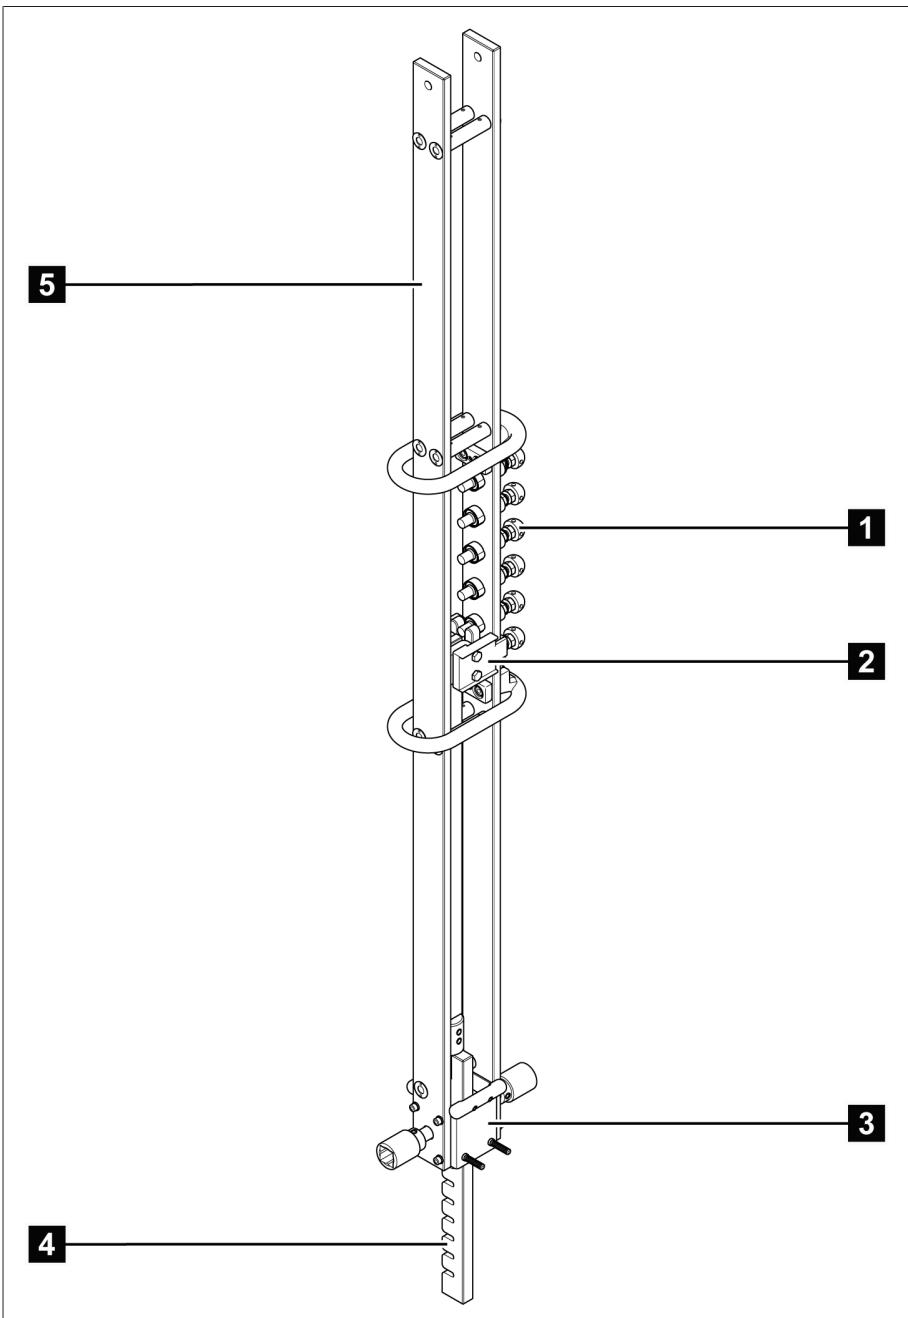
DEETAP® SPTM 025 с боковым расположением контактов
